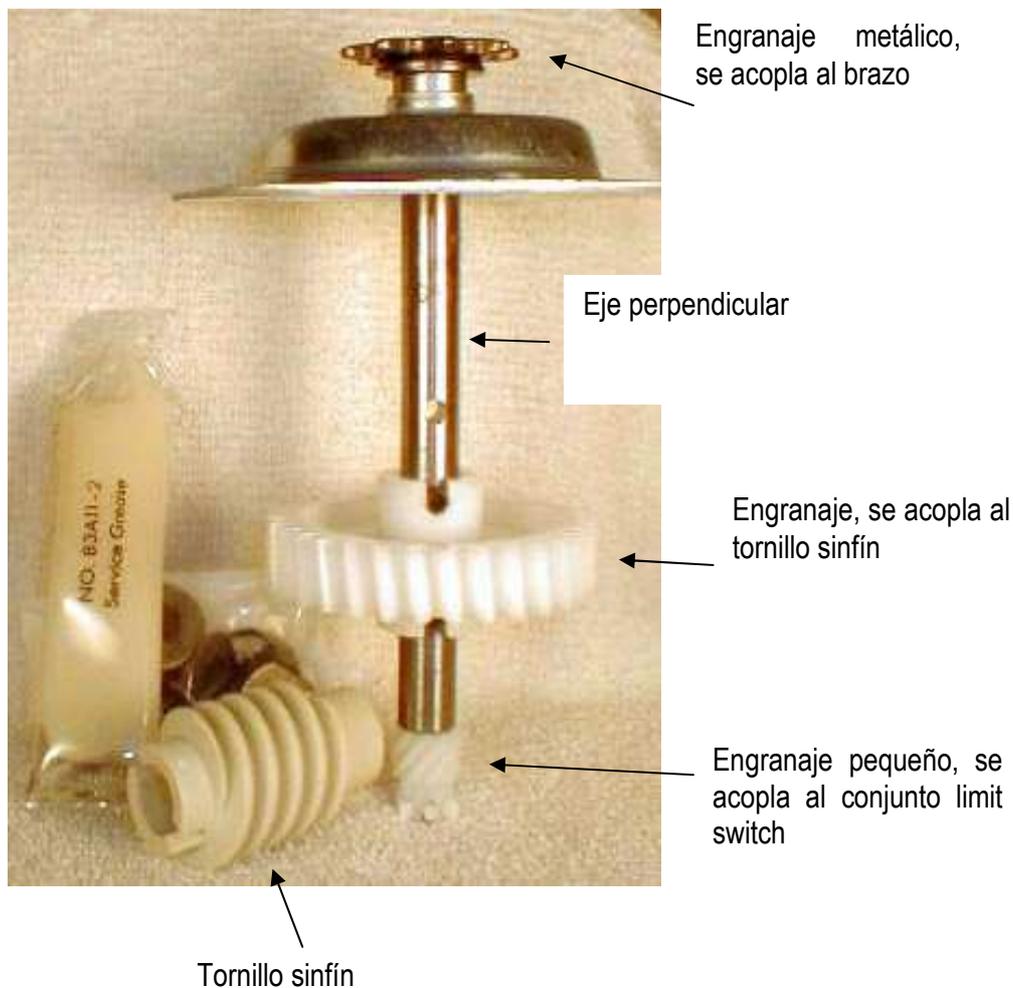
Elementos del reductor: eje perpendicular y tornillo sinfín.
